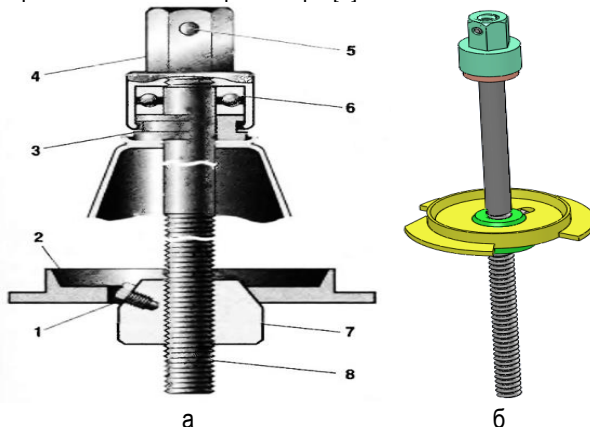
Пристосування для стиску пружин передньої підвіски:
